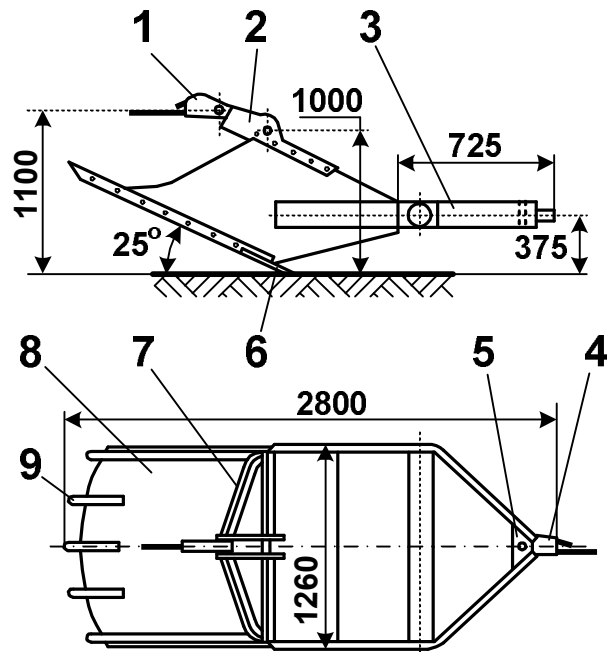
Совковый скрепер сварной конструкции с резцовым лезвием:
